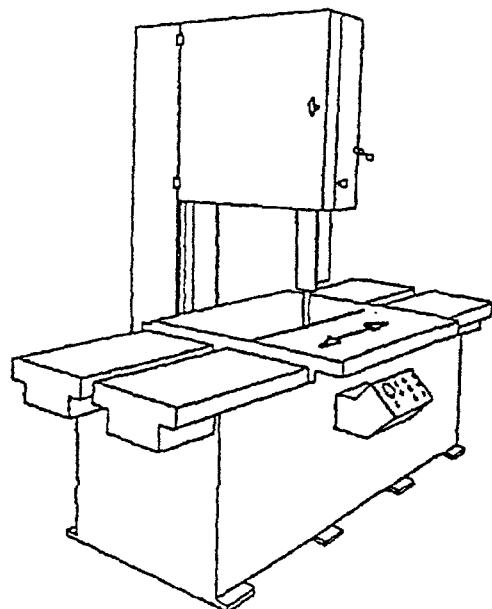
а — Вертикальний стрічковопиляльний верстат з траверсою та подаванням стола
